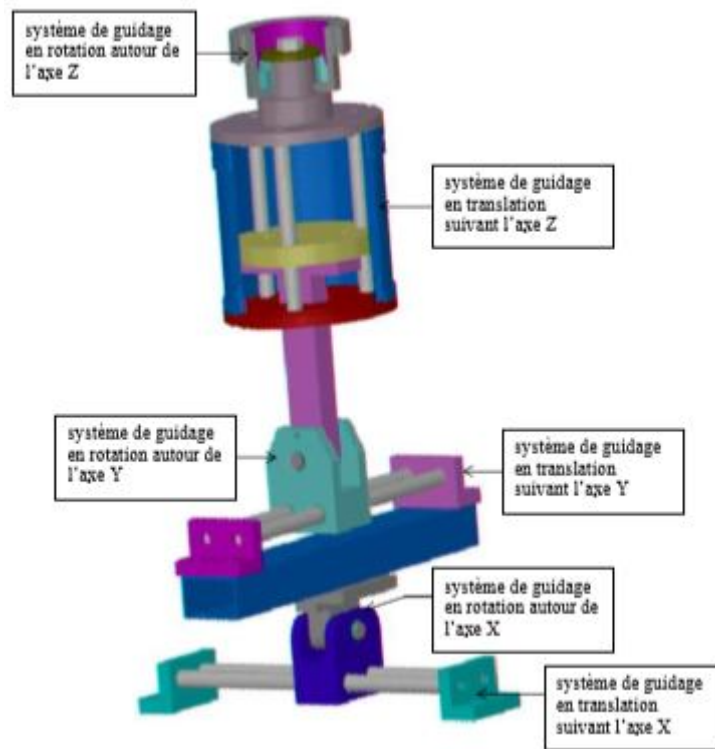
Vue d'ensemble du segment passif à multi-configurations
